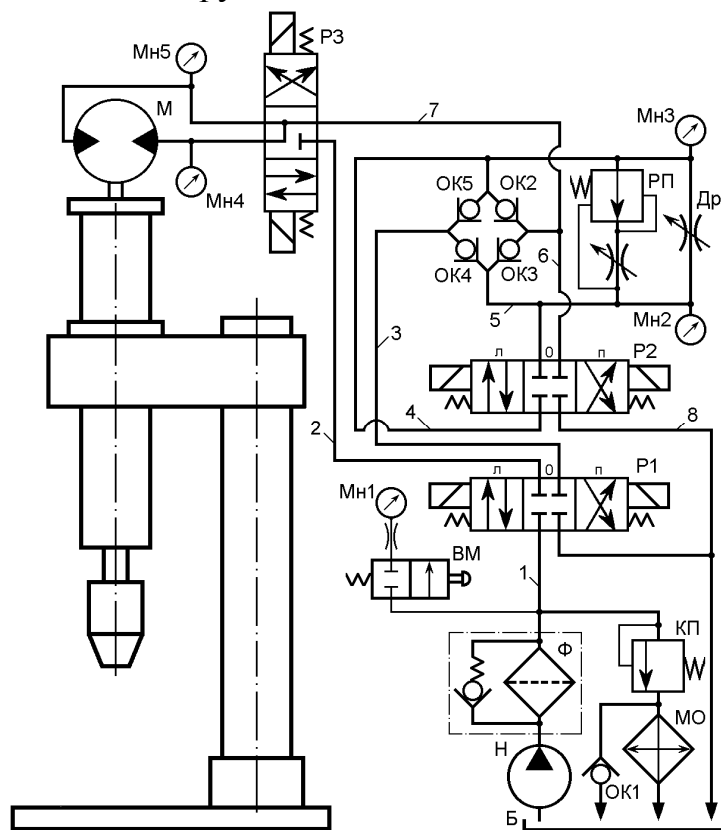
Схема сверлильного станка с гидравлическим приводом
